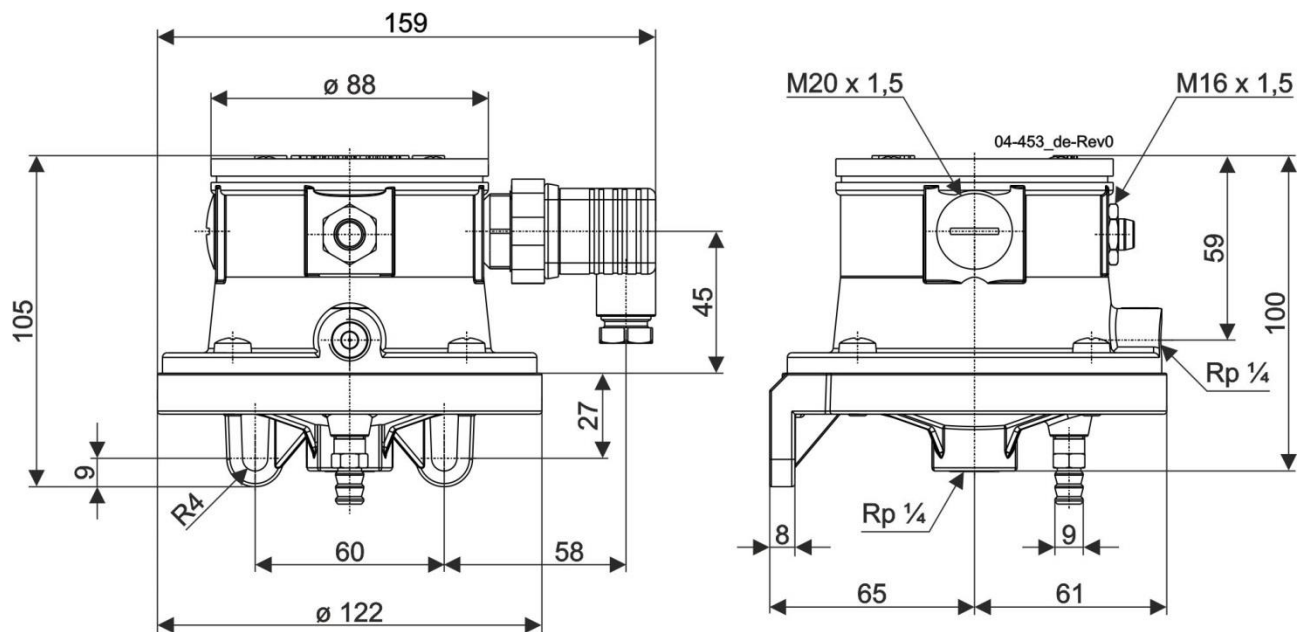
Maßblatt Druckwächter (Ausführung mit Signallampe und Gerätestecker 3 + PE)
